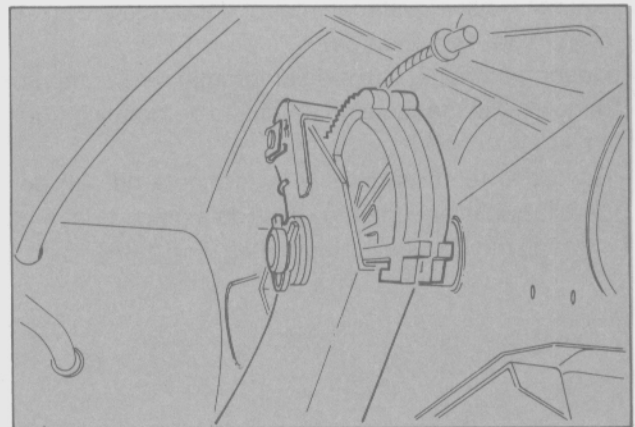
Desmontaje del cable de embrague del segmento dentado.
